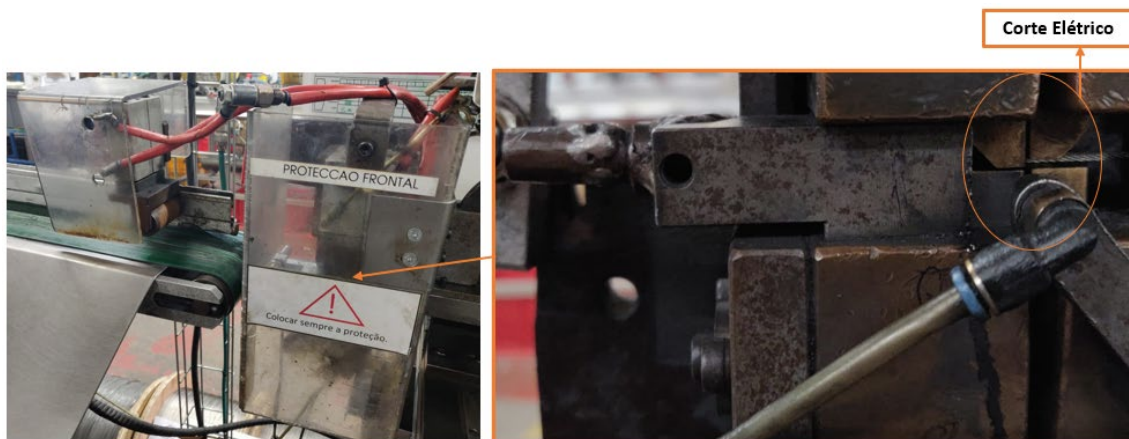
Sistema de corte elétrico na máquina de corte de cabo MCG00003F
